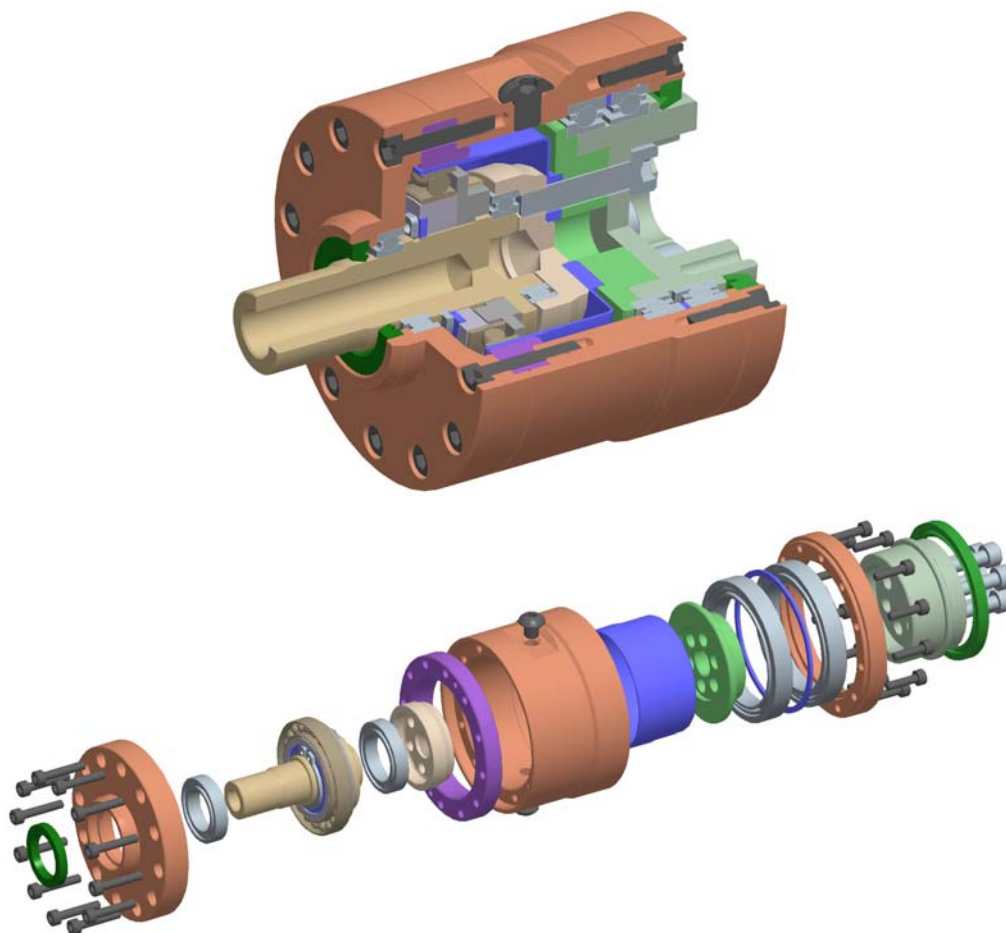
Vistes seccionada i explosionada del conjunt del reductor *HD
